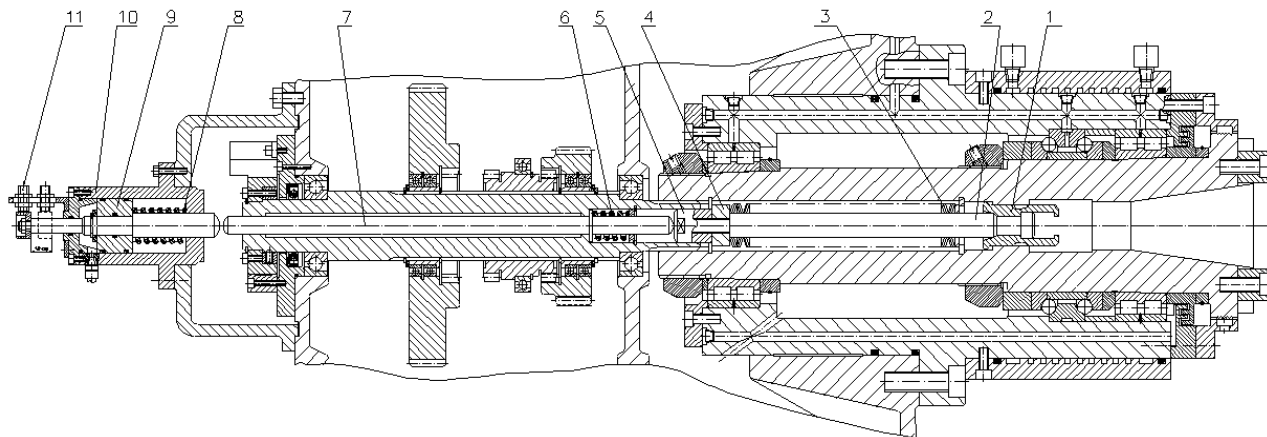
Механизм зажима и разжима инструмента многооперационного сверлильно-фрезерно-расточного станка с ЧПУ
